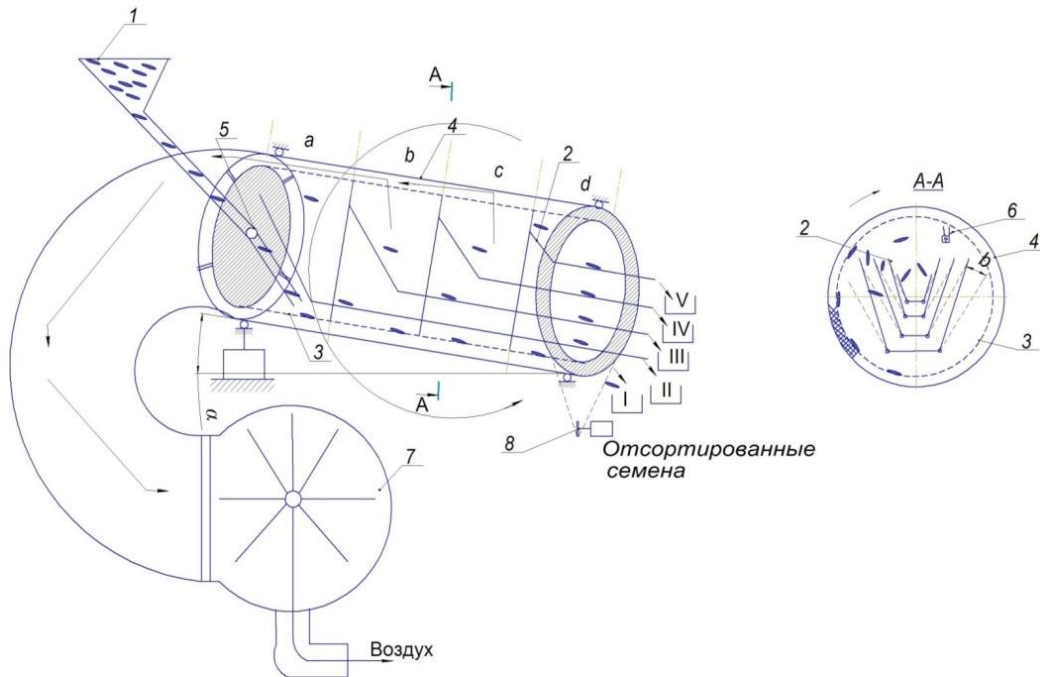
Схема разрабатываемого пневматического сепаратора: 1 – питатель; 2 – приемные лотки; 3 - перфорированный барабан; 4 – корпус сепаратора; 5 – отверстие для подачи семян; 6 – щетка; 7 – вентилятор; 8 – привод
